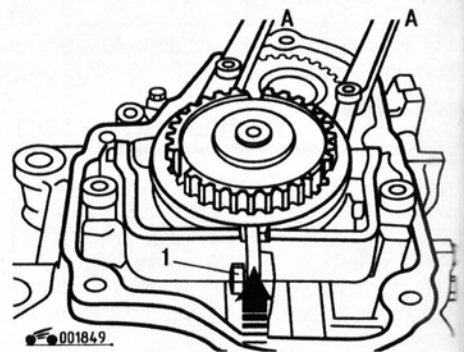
Регулировка положения вилки включения V передачи: А – щупы толщиной 1,2 мм; 1 – болт крепления рычага (стрелкой указано направление оттягивания вилки при регулировке)
